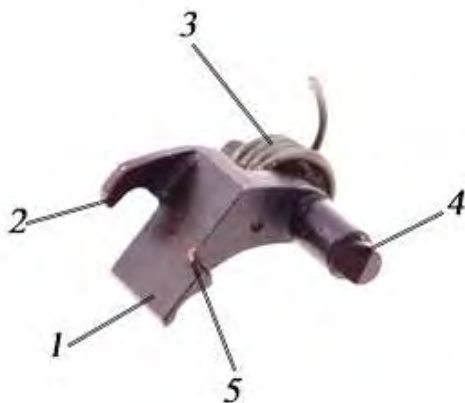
Шептало: 1 – широкий зуб; 2 – зуб; 3 – пружина шептала; 4 – цапфа; 5 – выступ
